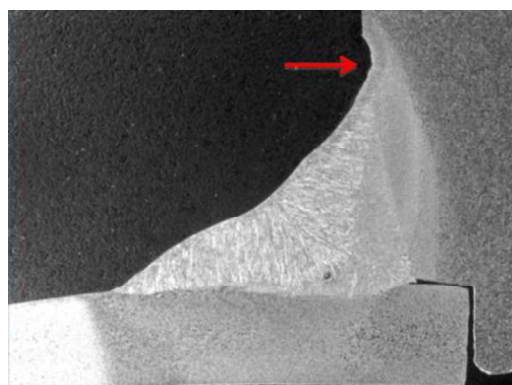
5 – Mordedura num canto de soldadura (Hadzihafizovic, 2022).
